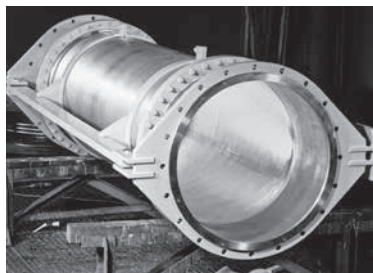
Lateral-Kompensator für Papiermaschinen
